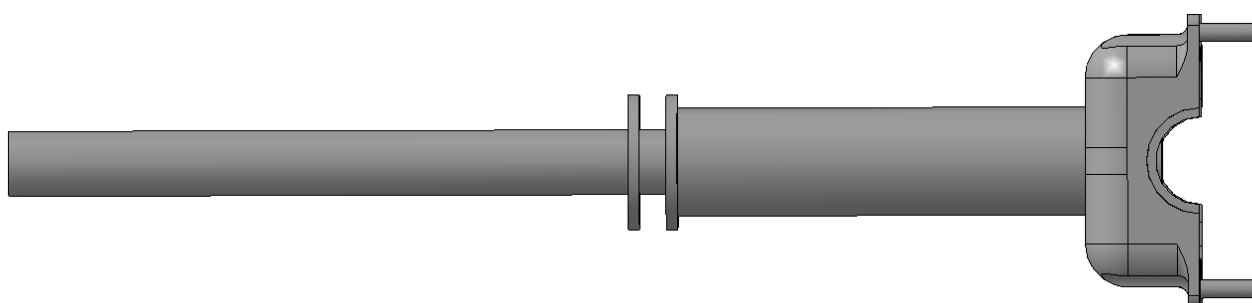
Вал приводной в сборе с нижней частью корпуса
